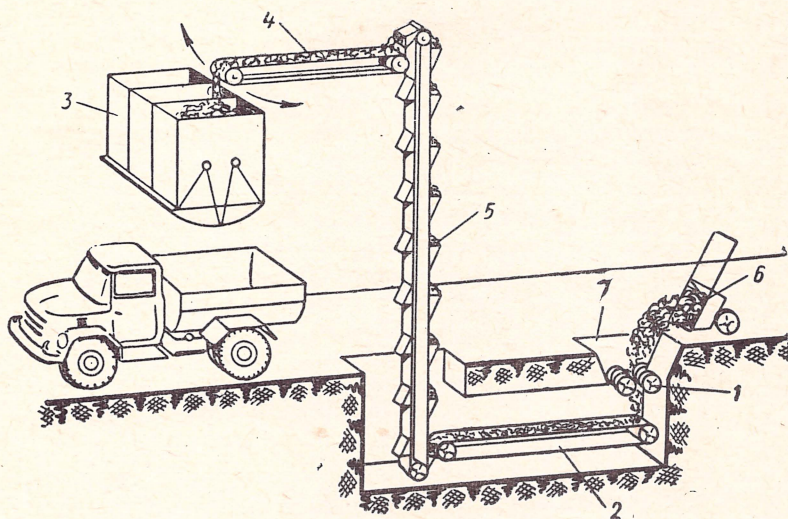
Установка для дробления, сбора и загрузки металлической стружки в автомашины
